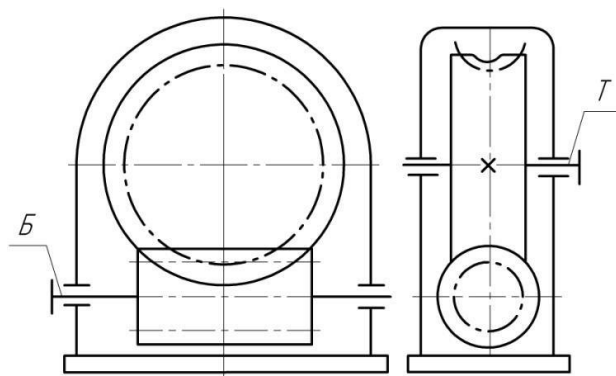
Червячный редуктор с нижним расположением червяка
